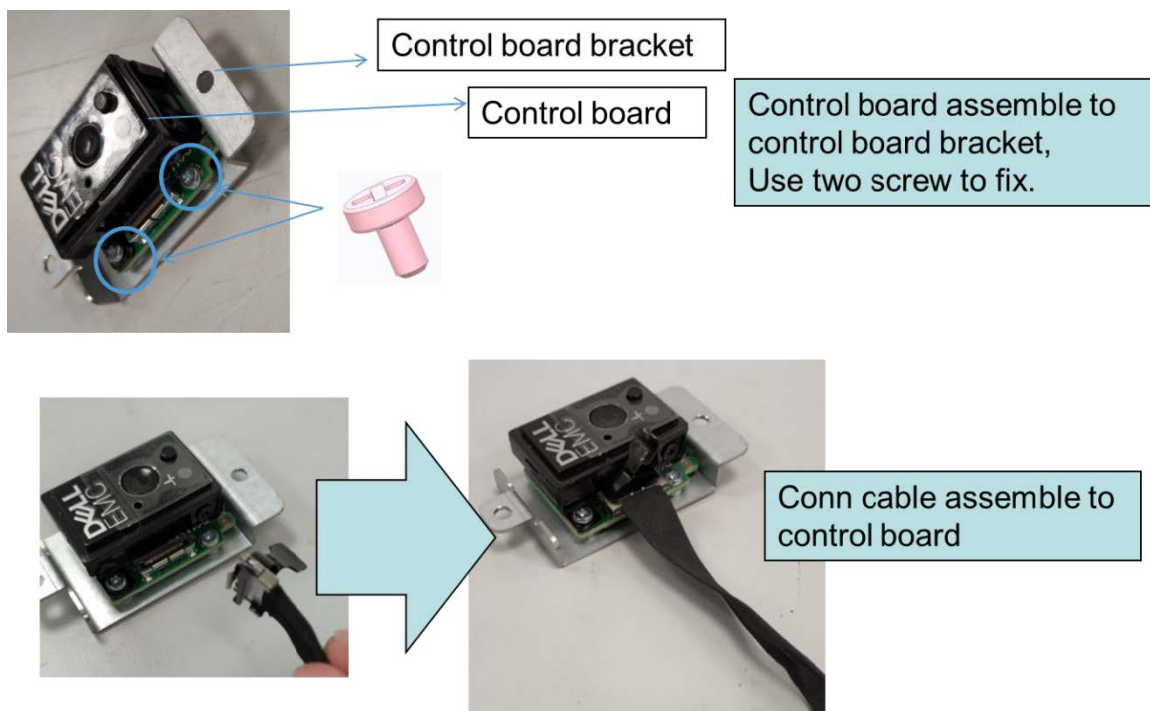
Panneau de commande et assemblage du câble de contrôle vers MB
